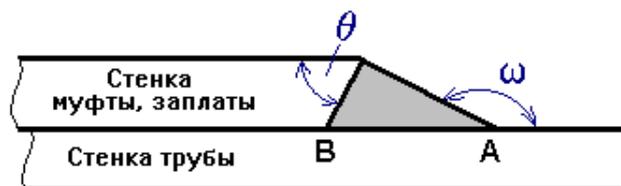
Форма сварного шва при установке ремонтной муфты
